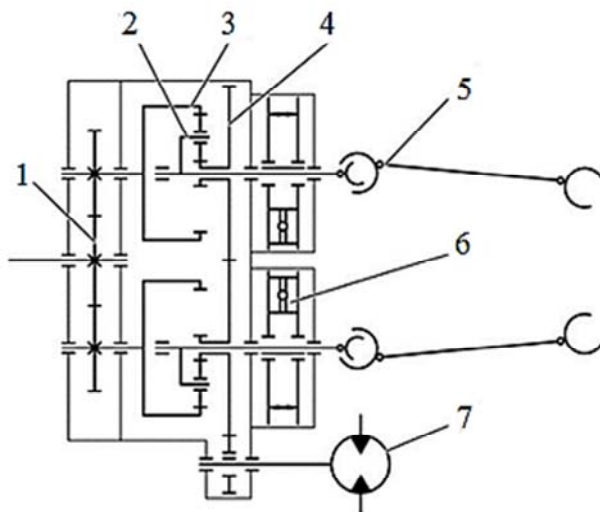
Кинематическая схема механизма поворота дифференциального типа:
